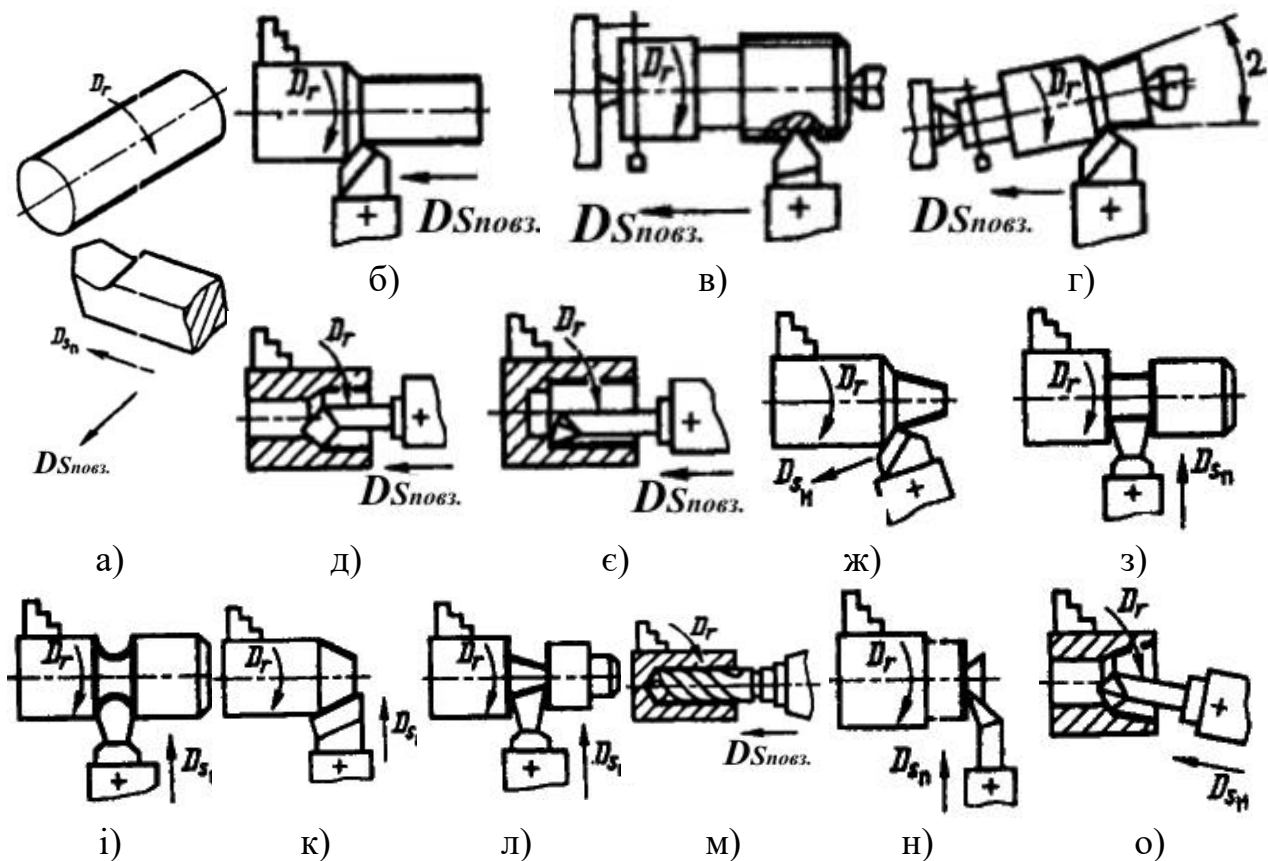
Типові схеми обробки поверхонь заготовок на верстатах токарної групи
